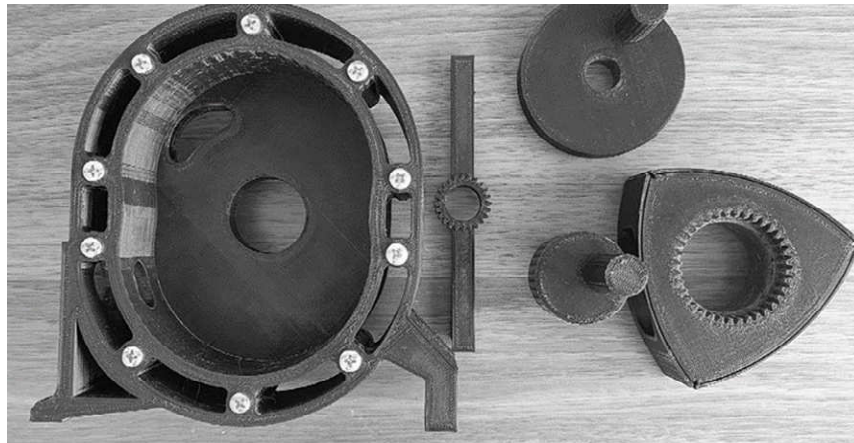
Все распечатанные детали роторного двигателя Ванкеля
